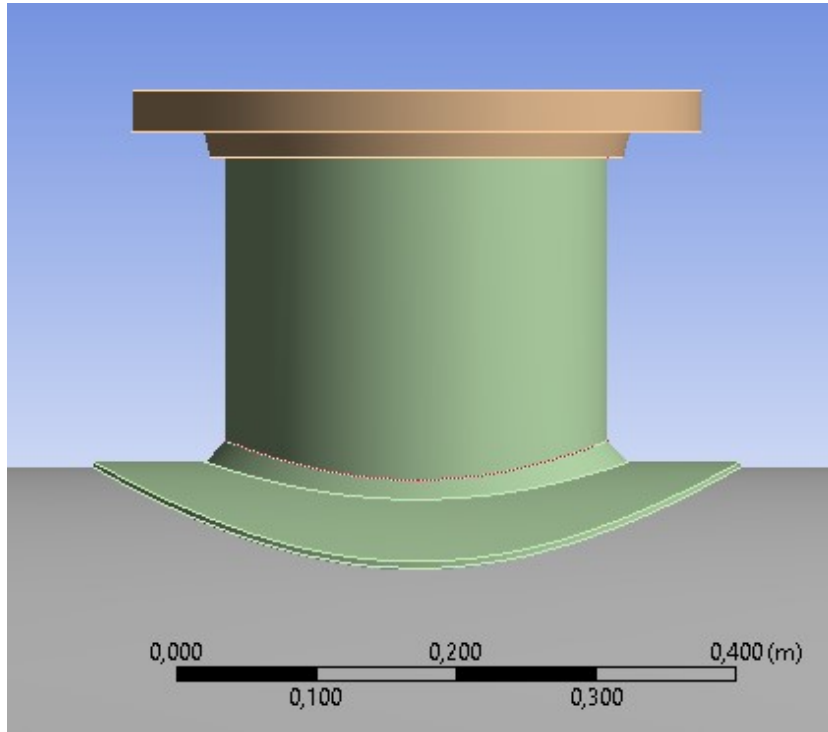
Modelación geométrica con incorporación de soldadura en la unión boquilla estanque.
